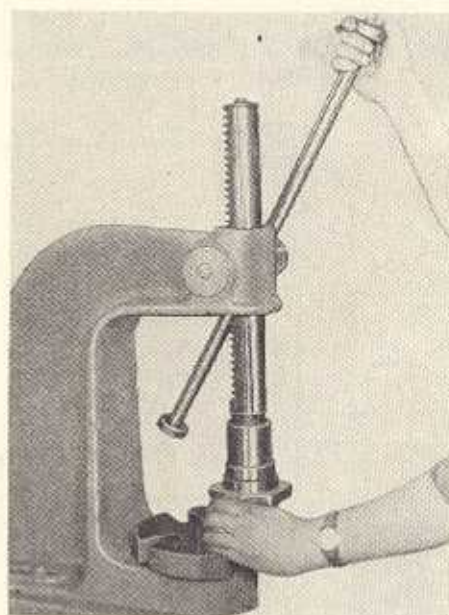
Einpressen des Rillenslagers 6307 in das Schwenklager (W-210 749)
